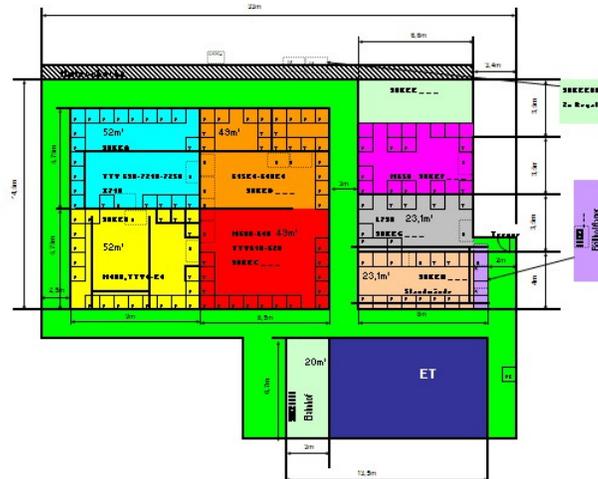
Layout das estações de pré-montagem dos sistemas de refrigeração.
